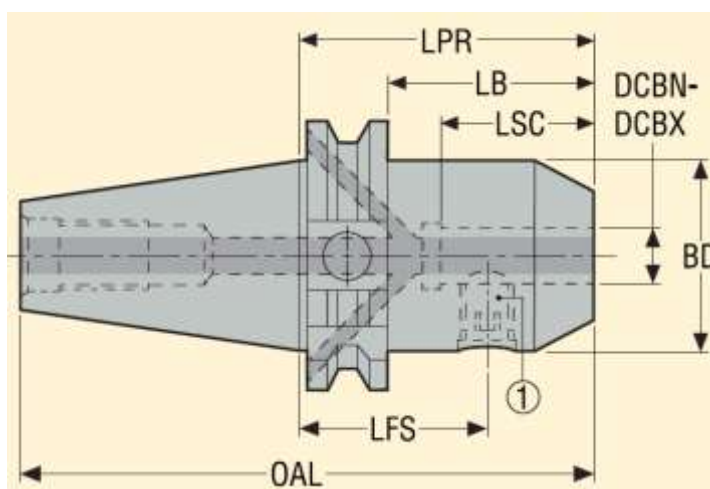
Державка для закрепления концевой шпоночной фрезы
